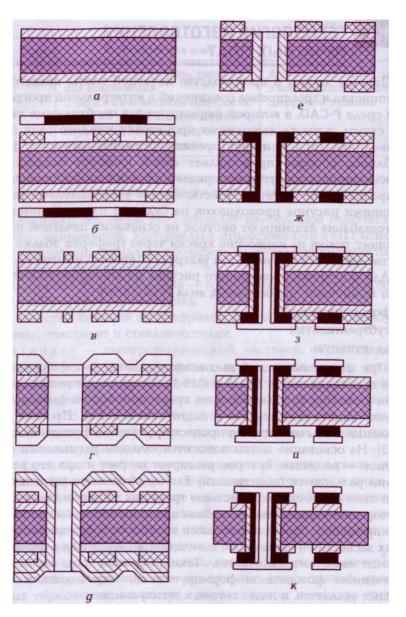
Этапы формирования проводников на печатных платах: а – заготовка из фольгированного диэлектрика; б – нанесение фоторезиста и экспонирование через фотошаблон; в – проявление защитного рельефа; г – нанесение защитного слоя и сверление отверстий; д – химическое меднение; е – удаление защитного слоя; κ – гальваническое осаждение меди; s – гальваническое нанесение защитного покрытия; s — удаление фоторезиста; s — стравливание фольги
